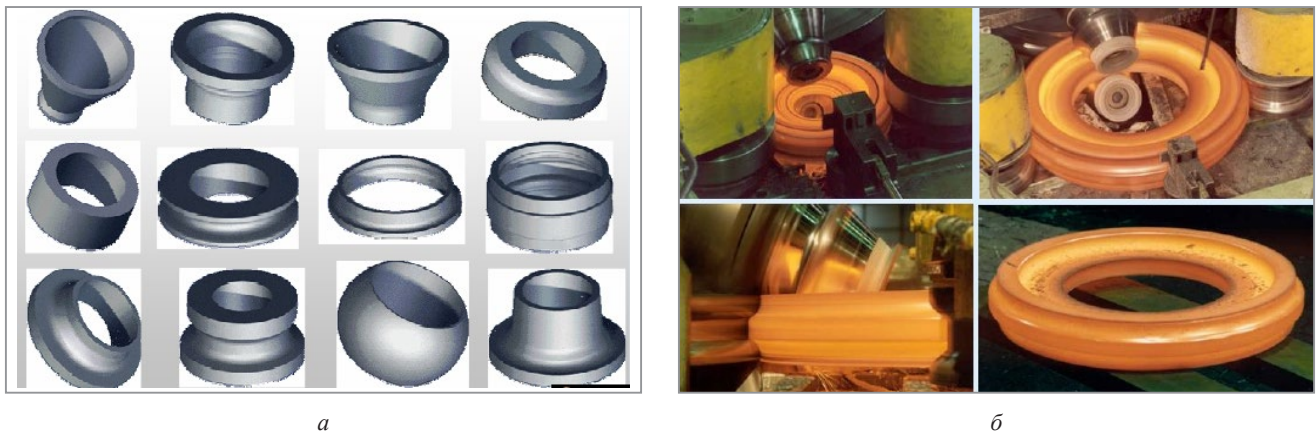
Возможности кольцеразкатки: *а* – номенклатура деталей для кольцеразкатки; *б* – разкатка профильных колец
